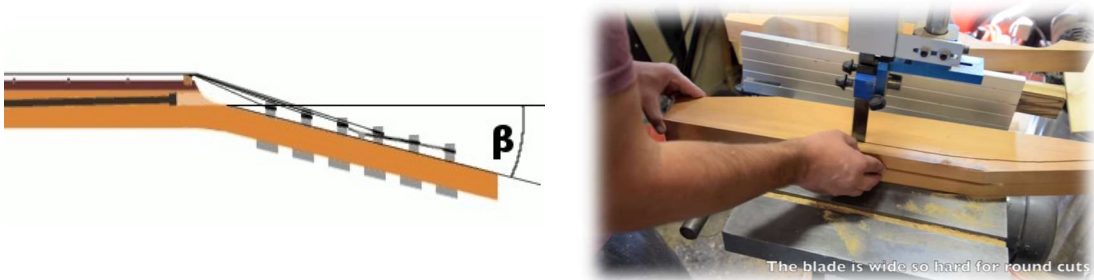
Esquema de un mástil con clavijero angulado (izquierda) y su manufactura a partir de una sola pieza de madera (derecha)
